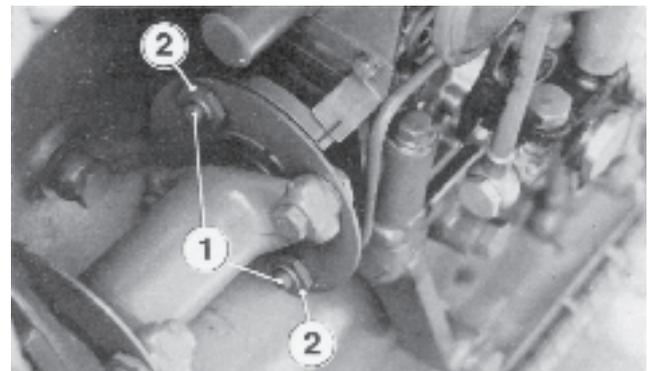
Accouplement de pompe (plaque de protection déposée)
